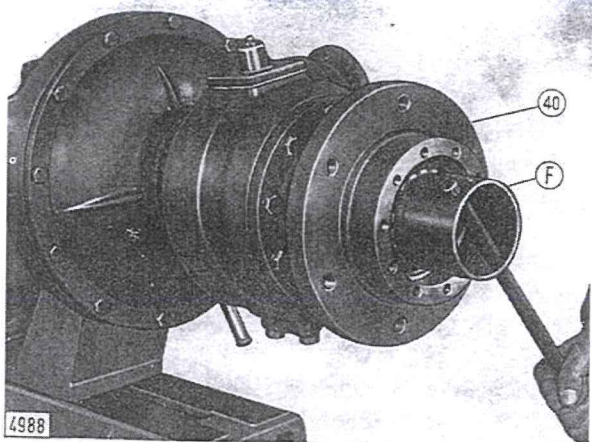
Smontaggio delle ghiere di fissaggio mozzo.
